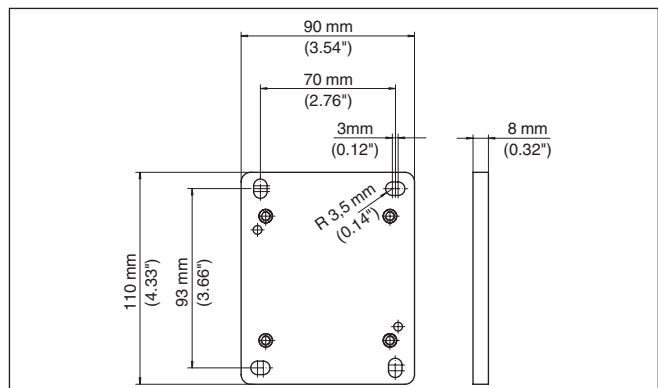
Boorplan - wandmontageplaat (externe behuizing)
